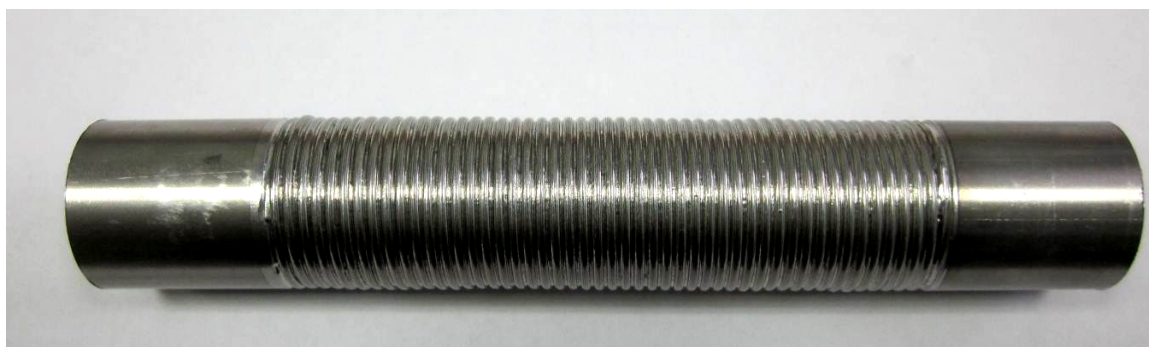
Внешний вид образца-свидетеля пружинно-витого канала теплообменного аппарата
